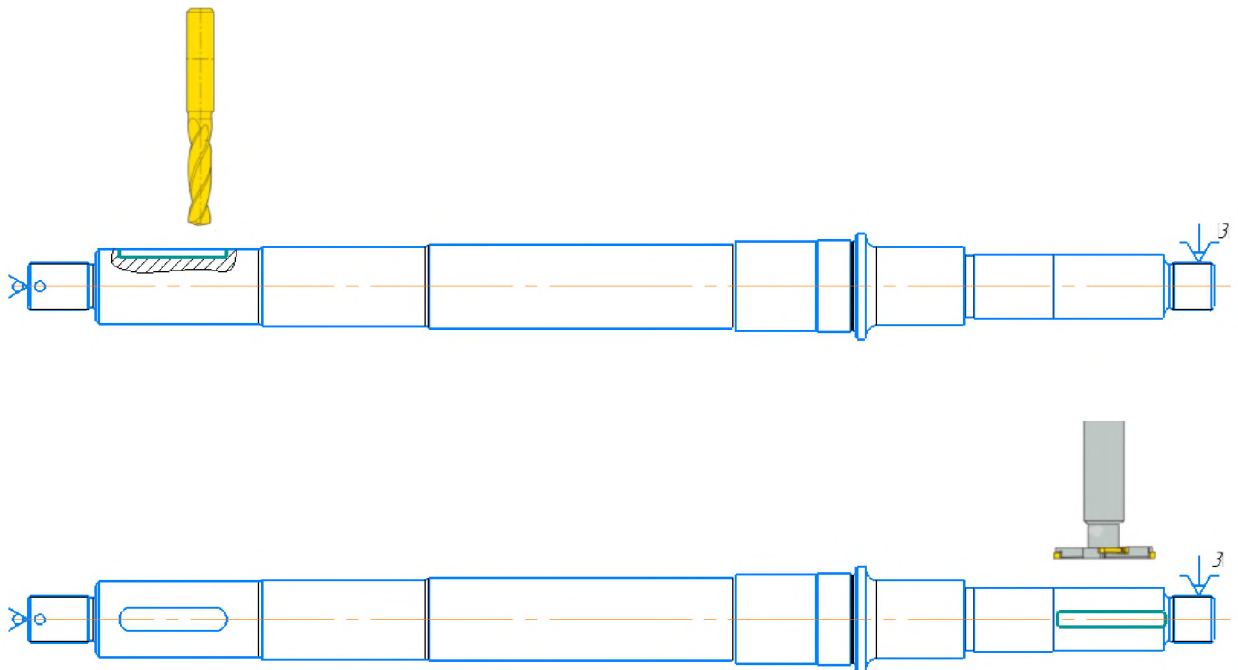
Технологічна схема базування другого варіанту встановлення заготовки (поворот валу)
